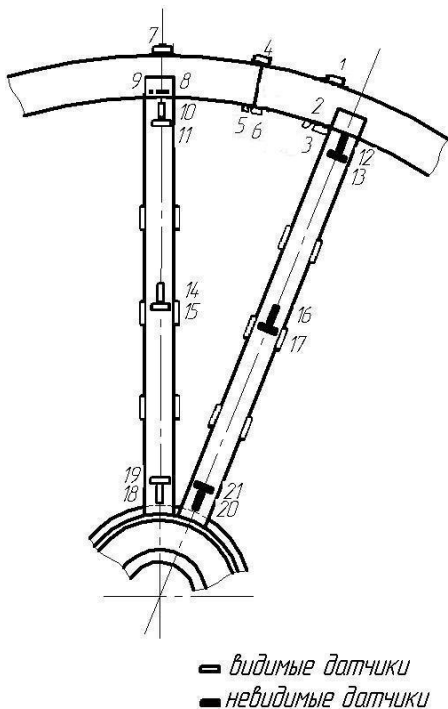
Схема расположения тензорезисторов на сварном шкиве
